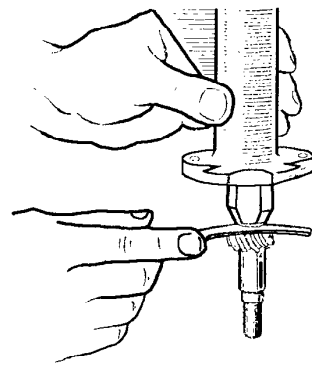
Проверка осевого зазора между корпусом привода масляного насоса и датчиком-распределителем зажигания с шестерней
